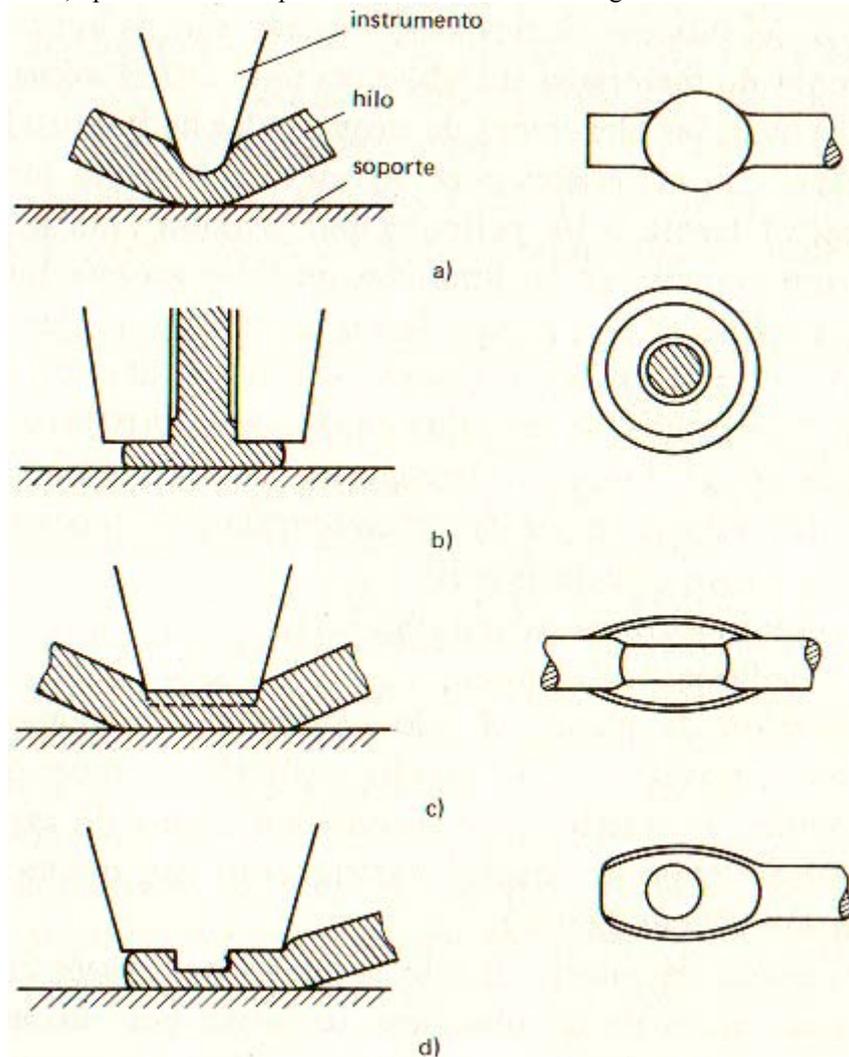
Tipos fundamentales de uniones por Termocompresión: (a) Uniones en forma de punto plano de soldadura: termocompresión en cuña; (b) Uniones en forma de cabeza de clavo: termocompresión por capilar con formación de bolita; (c) Unión con costilla de refuerzos: termocompresión a base de instrumento con ranura o electrodo partido; (d) Uniones tipo "ojo de pez": termocompresión a base de instrumento con un saliente. [9]
